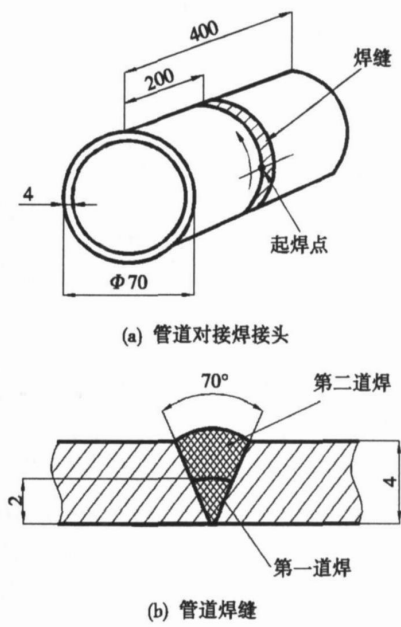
管道对接焊接头和管道焊缝 (mm)
